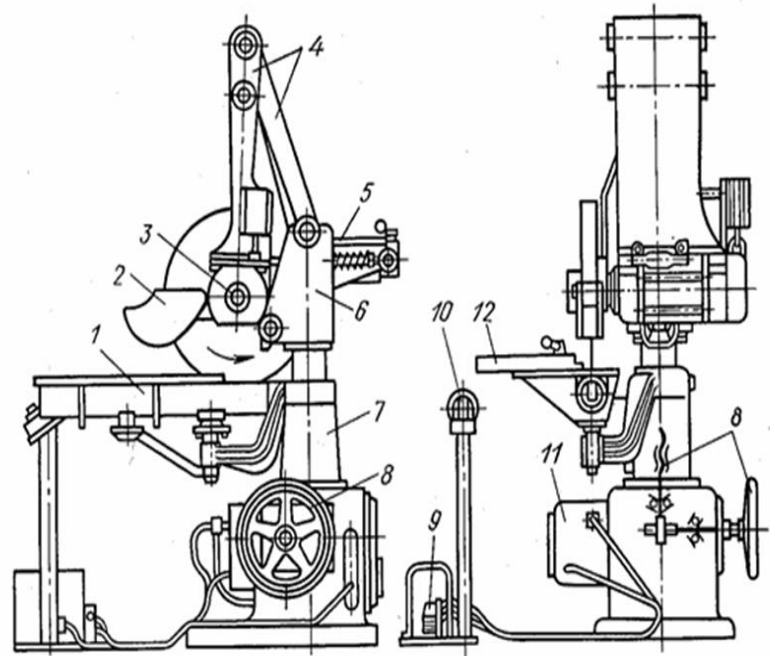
Схема торцовочного станка ЦМЭ-3А:
